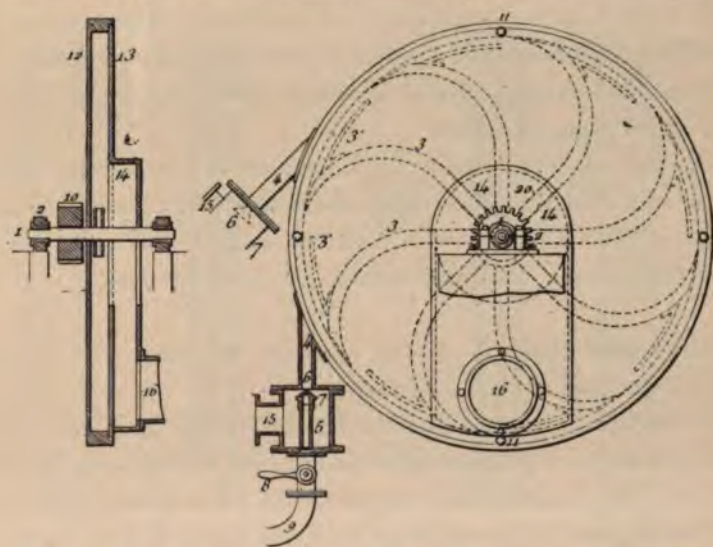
et 38. — Turbine à vapeur Pelletan. Coupe et vue d'ensemble.
